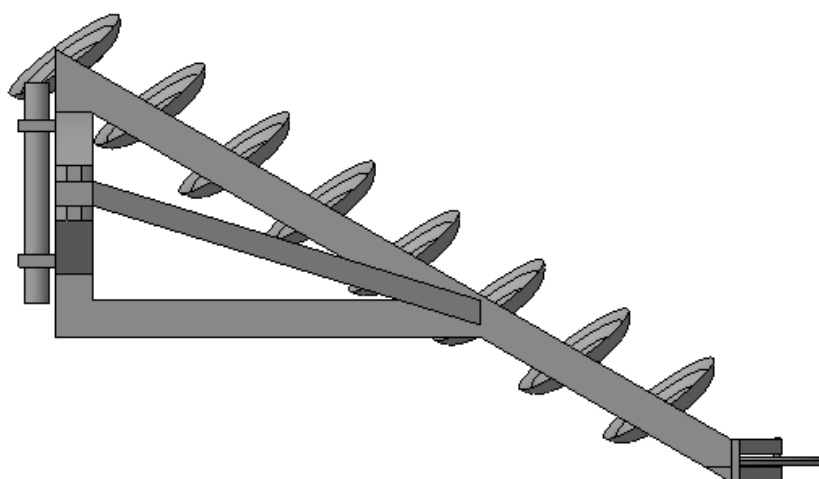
Предлагаемая конструкция плуга. Вид сверху
